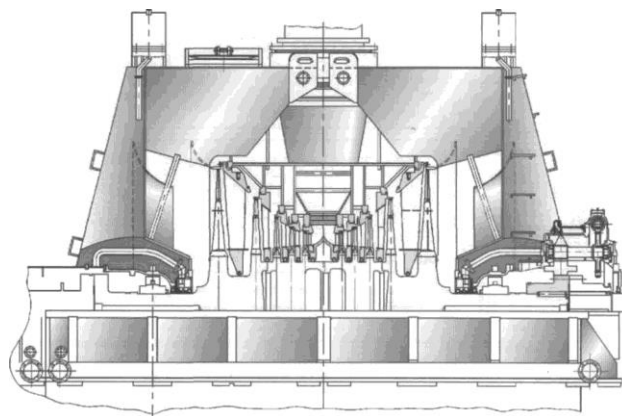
Общий вид ЦНД паровой турбины К-325-23,5
